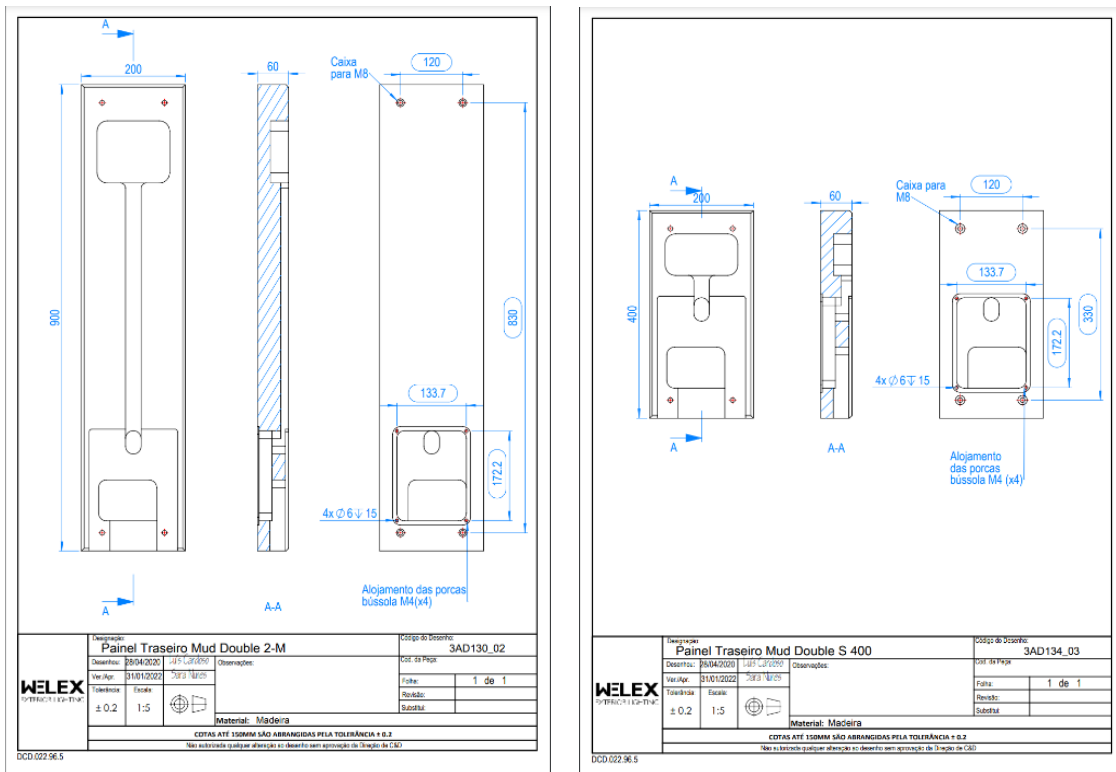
Conjunto de imagens do desenho técnico dos candeeiros a desenvolver.
